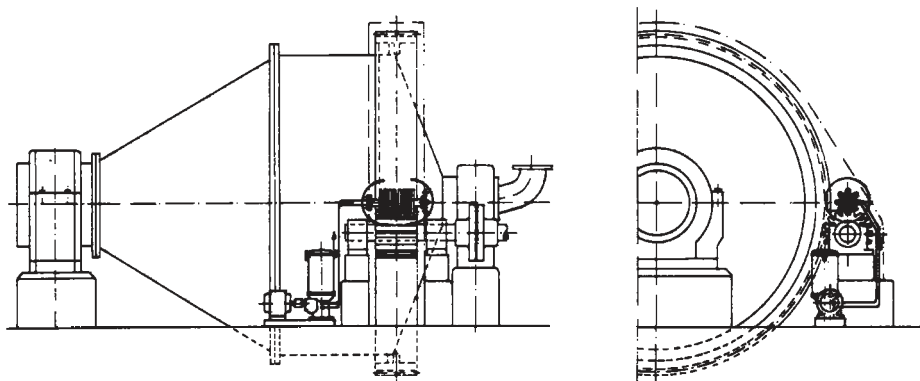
Смазка зубчатой шестерни на мельнице ГОКа
